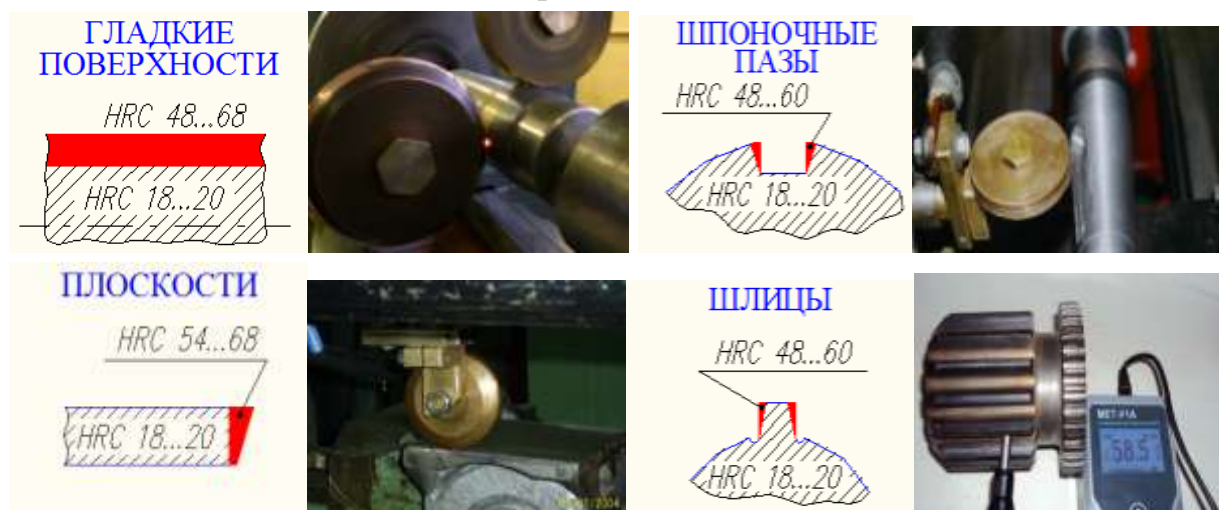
Принципиальные схемы и фрагменты ЭМПЗ поверхностей деталей
